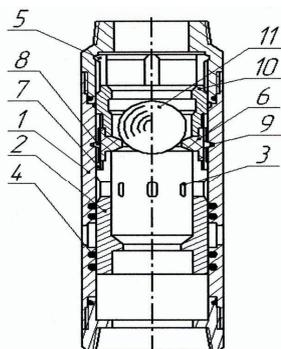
Циркуляционный клапан: 1 - корпус с переводником; 2 - подвижная втулка с нижним седлом; 3 - циркуляционные отверстия в корпусе и втулке; 4 - уплотнительные элементы; 5 - фиксатор крайних положений; 6 - эластичный штуцер; 7 - цанговая втулка; 8 - кольцевой выступ; 9 - проточка в корпусе; 10 - поджимная втулка; 11 - управляющий шар
